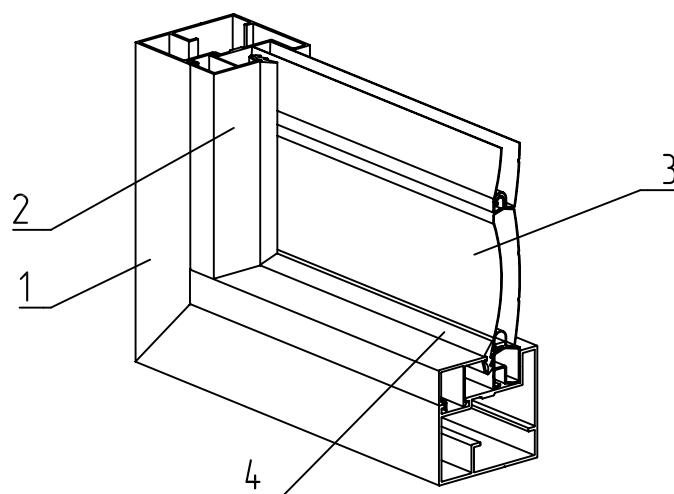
Установка штапика FLGU.400.0304 и уплотнителя в створку калитки
